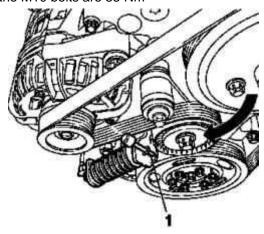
Ослабление натяжителя поликлинового ремня: 1 – специальный инструмент
